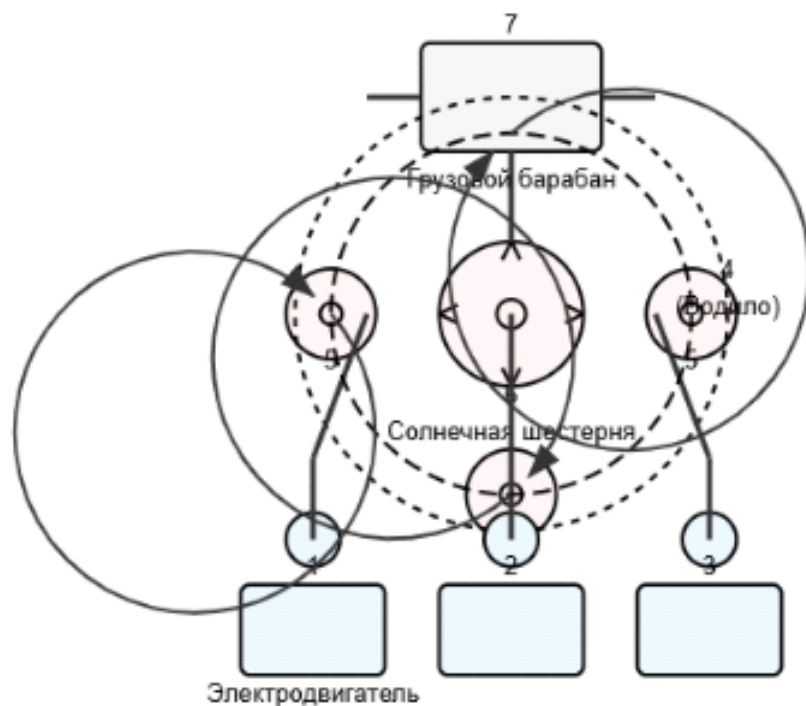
Кинематическая схема многодвигательного привода: 1, 2, 3 – электродвигатели; 4 – планетарный редуктор (водило); 5 – сателлиты; 6 – центральная (солнечная) шестерня; 7 – грузовой барабан.
